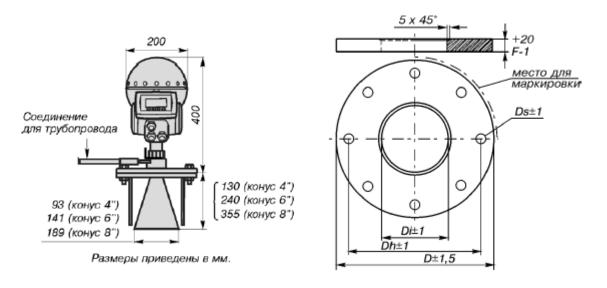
Габаритно-установочные размеры Rosemount 5600
